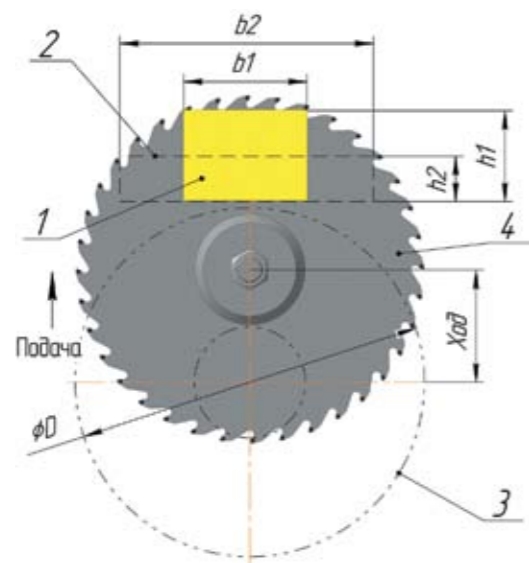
Рабочий цикл (вертикальная подача): 1 – заготовка № 1; 2 – контур заготовки № 2. Положения торцовочной пилы: 3 – исходное; 4 – конечное
